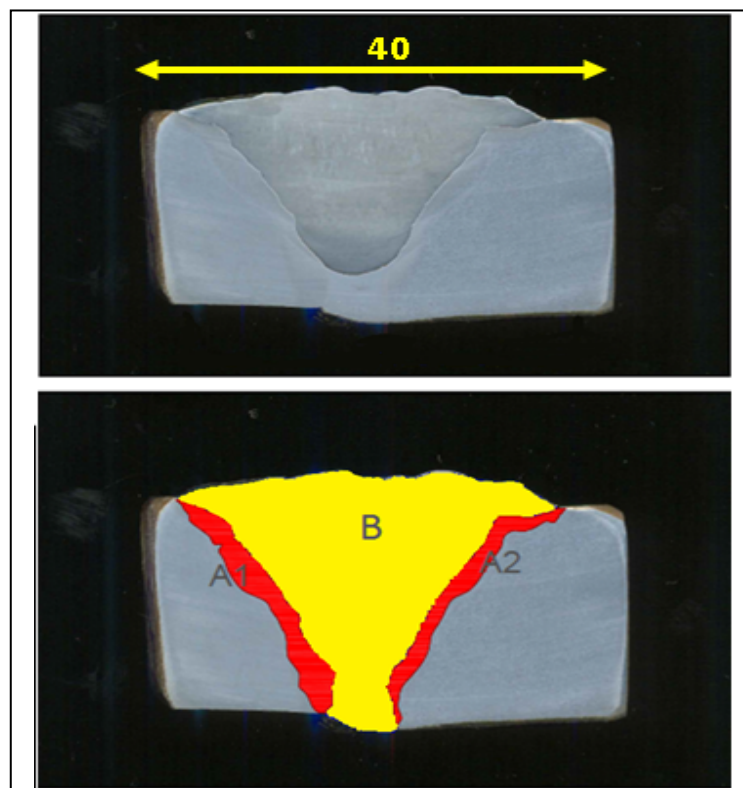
Secção transversal do Corpo-de-prova Soldado com inox.
